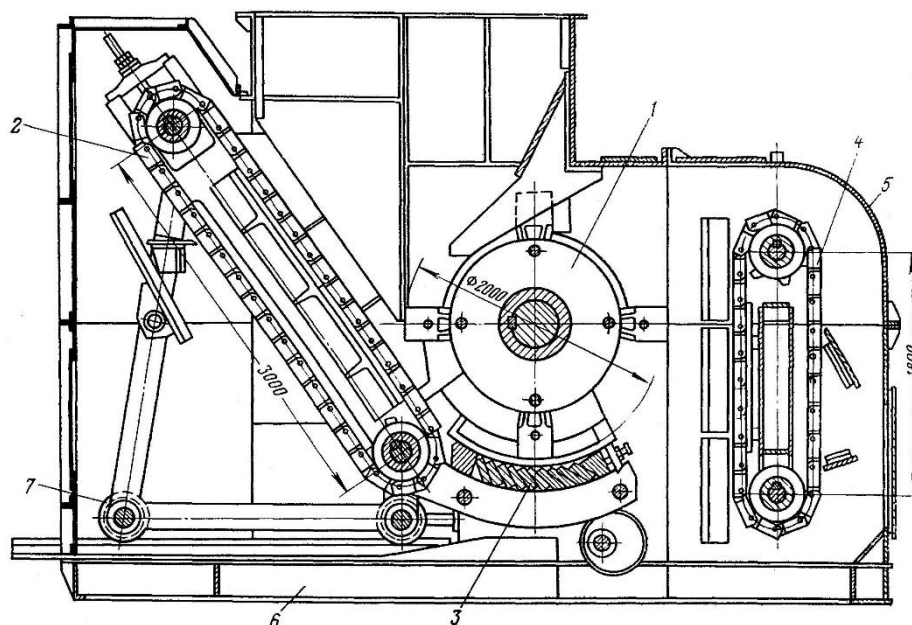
Молоткова дробарка з убудованими важкими пластинчастими конвеєрами та колосниковою решіткою [16, 17, 21]: 1 - ротор; 2 - подавальний конвеєр; 3 - колосникова решітка; 4 - очисний конвеєр; 5 - корпус дробарки; 6 - опорна плита; 7 - катки рами подавального конвеєра.
